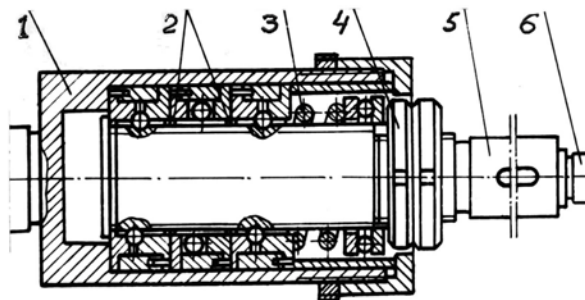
Конструкція запобіжного патрона навантажень інструмента
